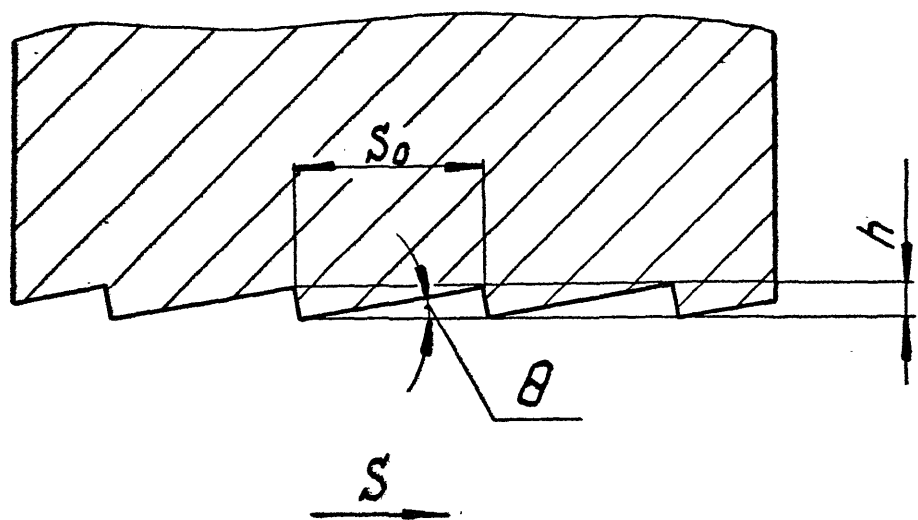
Профиль поверхности, обработанной резцом с прямолинейной режущей кромкой.
